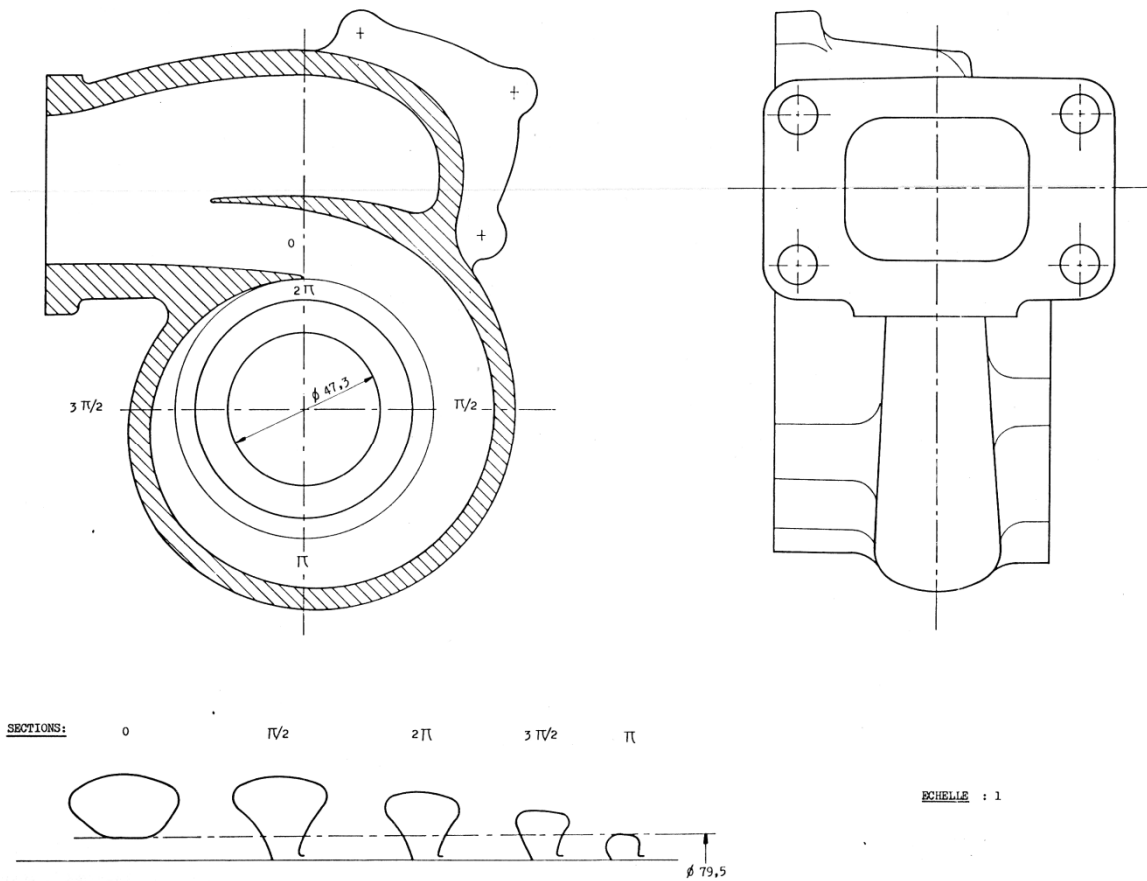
Ensemble carter turbine du turbocompresseur [55]
